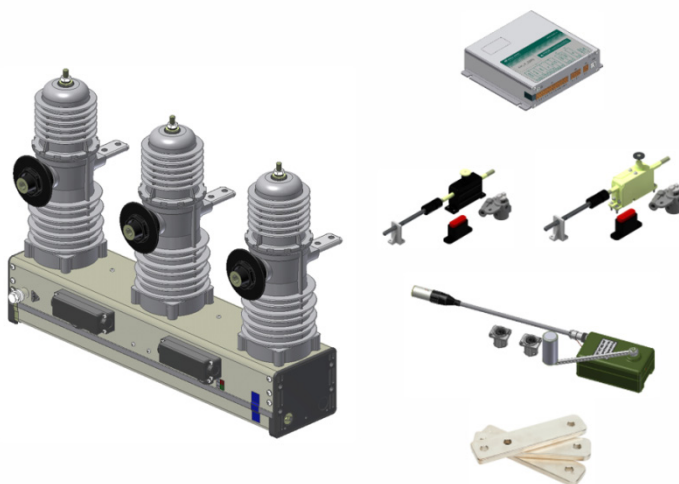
Общий вид выключателя TER_VCB25_LD1_F
